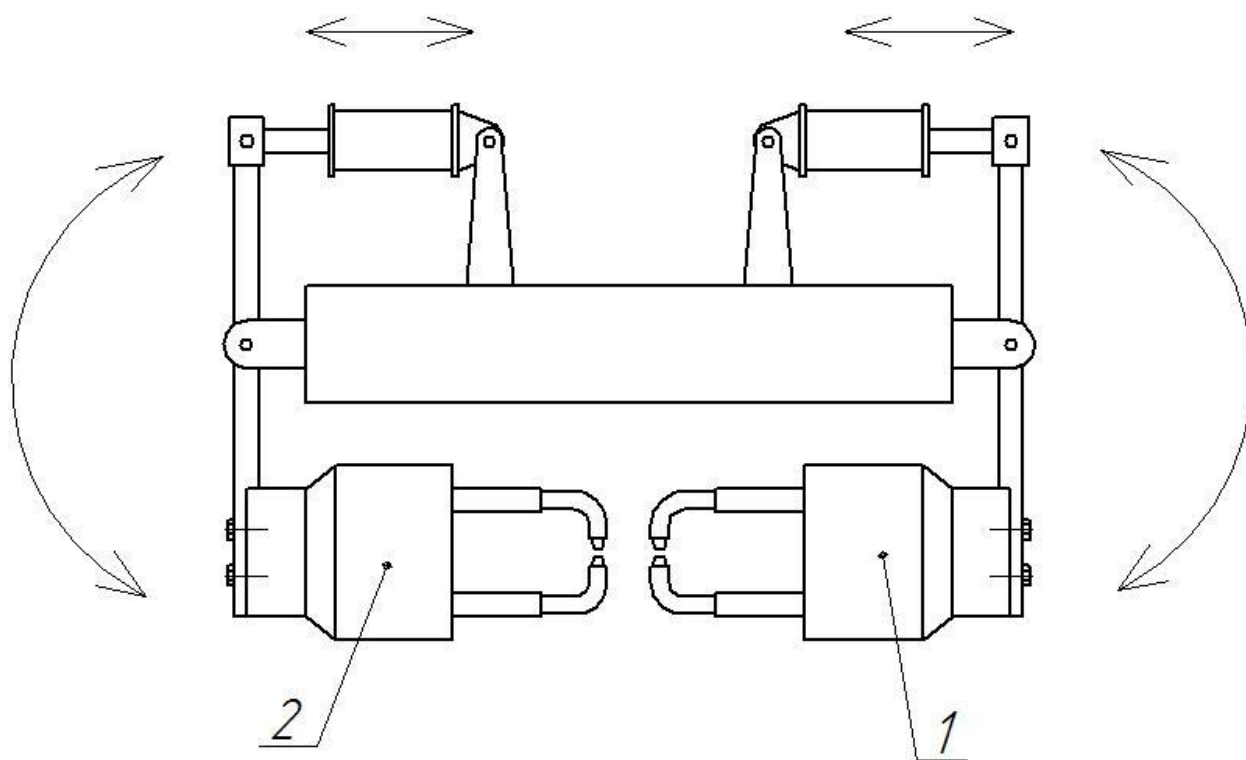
Подача сварочных групп 1 (5 клещей) и 2 (5 клещей) к месту сварки
